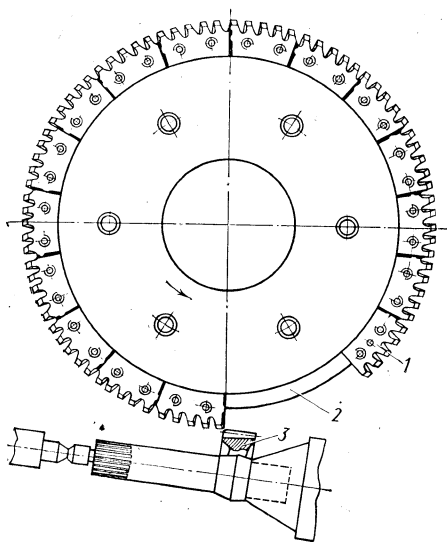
Схема обработки зубчатого колеса: 1 — резцовый блок; 2 — свободная часть сектора инструмента; 3 — зубчатое колесо
